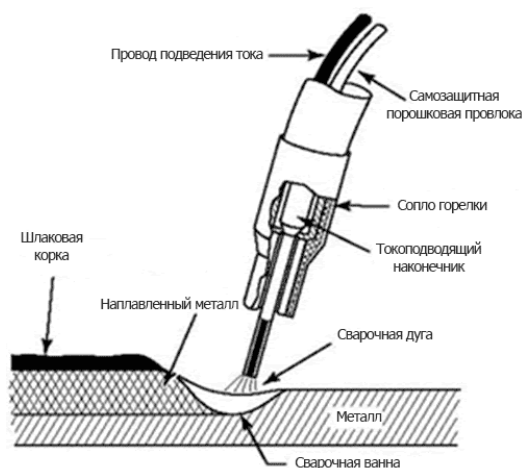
Схема выполнения сварки порошковой самозащитной проволокой
